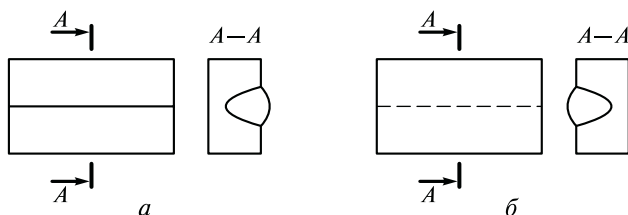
Изображение сварных швов на чертежах:
